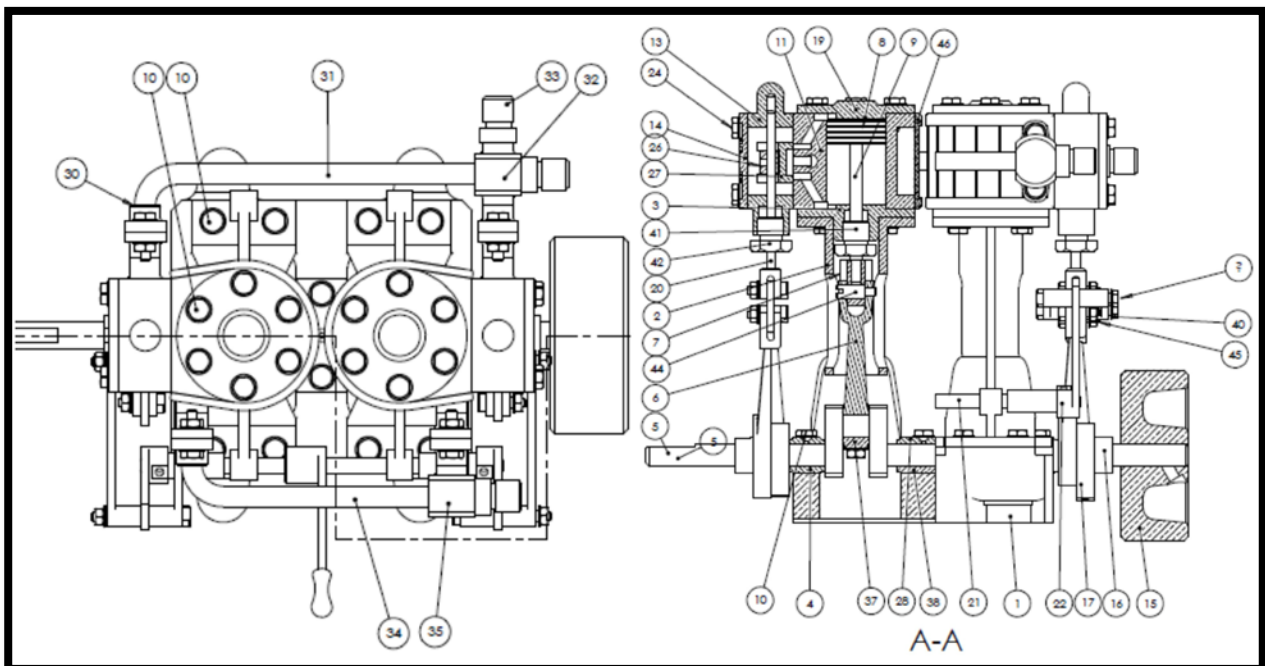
Vistas de planta (izquierda) y alzado (derecha) del motor
